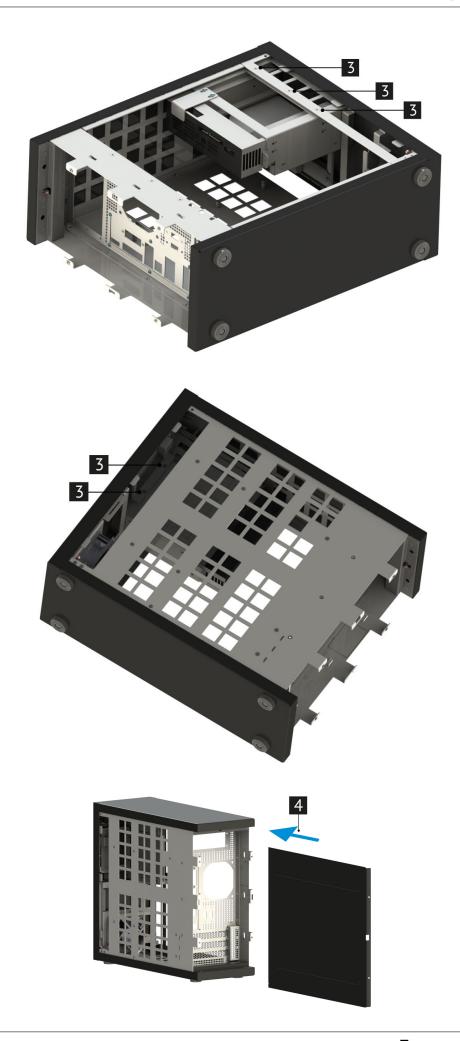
Установка каркаса отсека 5'25 в рабочую станцию
